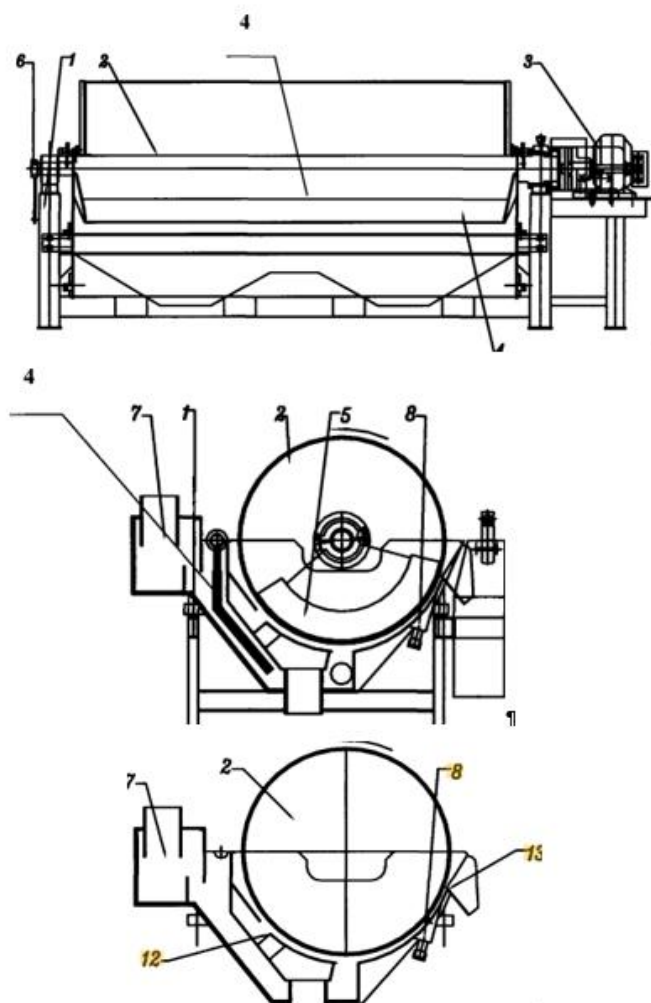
Мокрий магнітний сепаратор для дрібних частинок барабанного типу з постійними магнітами
